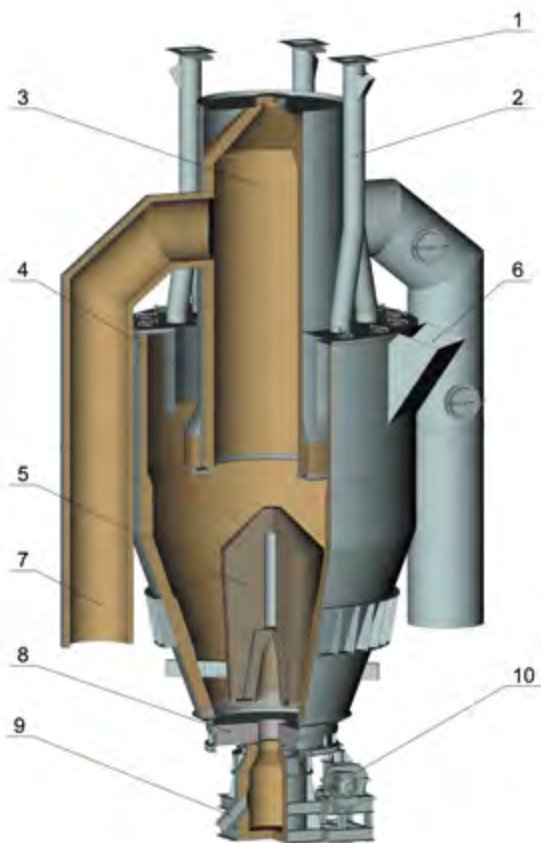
Шахтный противоточный подогреватель известняка для установки на реконструированной печи взамен перекрестно-точного подогревателя с парoisпарительным контуром: 1 – затворы штыревые; 2 – точки загрузочные запорные; 3 – камера газораспределительная; 4 – тетка кольцевая распределительная; 5 – вставка огнеупорная; 6 – газоход отводящий; 7 – газоходы подводящие; 8 – устройство выгрузочное; 9 – тетка подачи нагретого известняка; 10 – привод выгрузочного устройства
